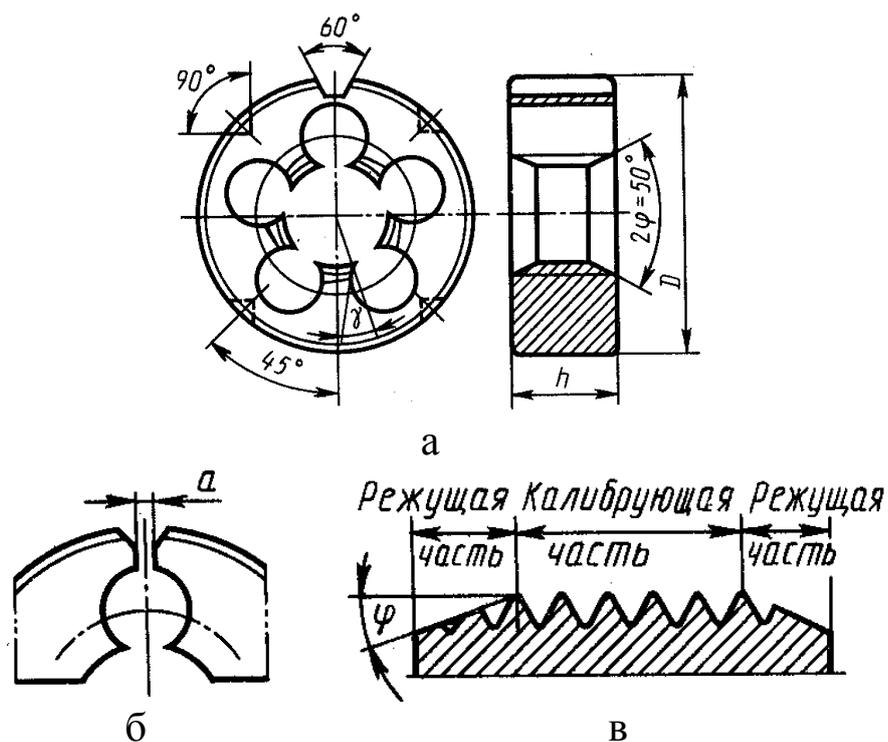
Части и элементы круглой плашки: а - круглая плашка до разрезания; б - разрезанная круглая плашка; в - профиль резьбы рабочей части
